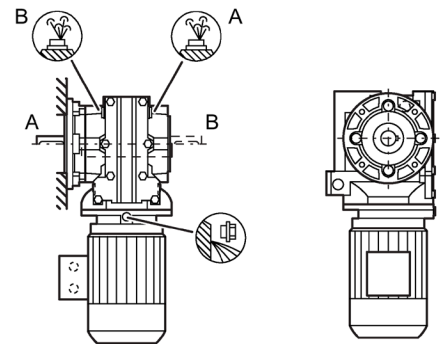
Einbaulagen für Stirnradschneckengetriebe CAD Aufsteckausführung Baugrößen 39 - 89
